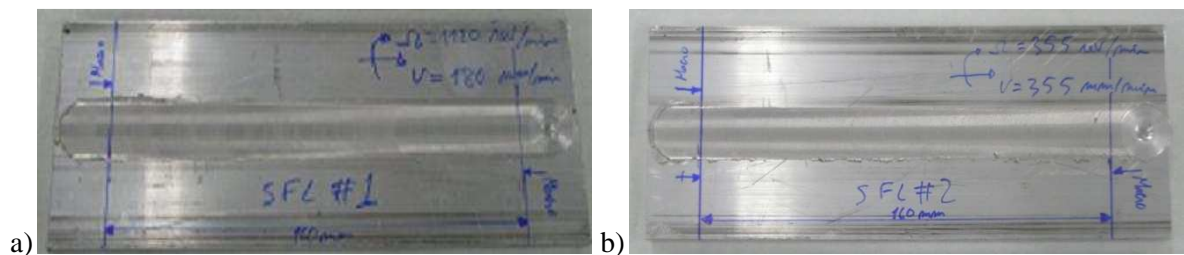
Chapas de alumínio da liga 1100 processadas por PFL; a) Cordão de Soldadura a quente; b) Cordão de Soldadura a frio.
